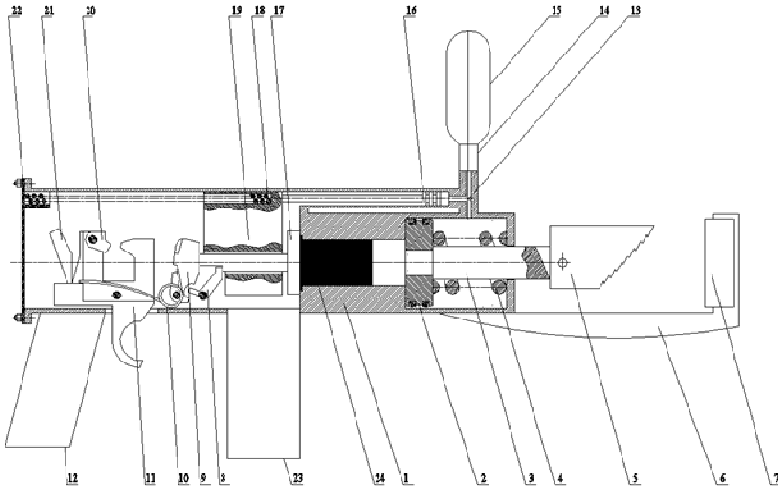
Швидкодіючий автономний ручний різак: 1 – корпус; 2 – поршень з ущільненнями; 3 – шток; 4 – зворотна пружина; 5 – фреза-ніж; 6 – Г-образна скоба; 7 – нерухомий ніж; 8 – шептало автоспуску; 9 – курок; 10 – пружина; 11 – спусковий гачок; 12 – ручка для утримання; 13 – газовідводна трубка; 14 – незворотній клапан; 15 – збірний балон; 16 – поршень штоку затворної рами; 17 – затвор з ударником; 18 – пружина; 19 – затворна рама; 20 – засувка словильнювача курка; 21 – запобіжник; 22 – задня кришка; 23 – магазин з набоями; 24 – набій
